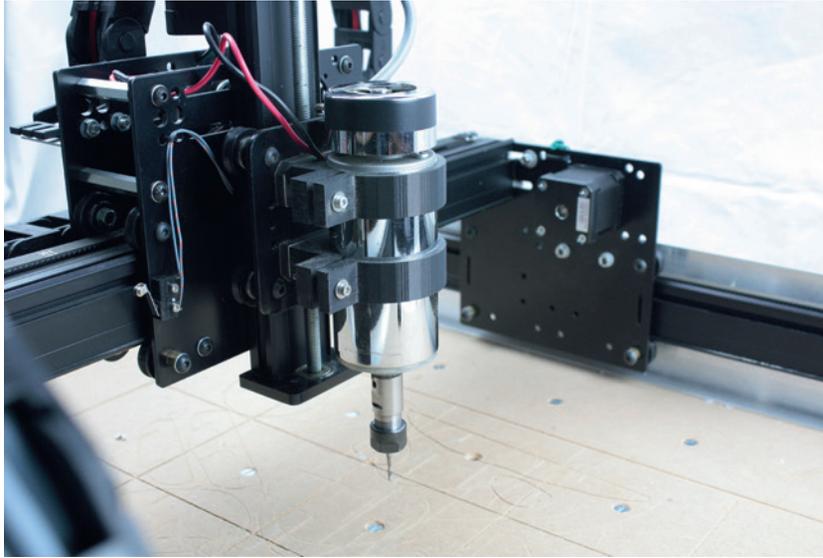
Die typische „Chinaspindel“, wie sie in Hobbyfräsen gerne eingesetzt wird
